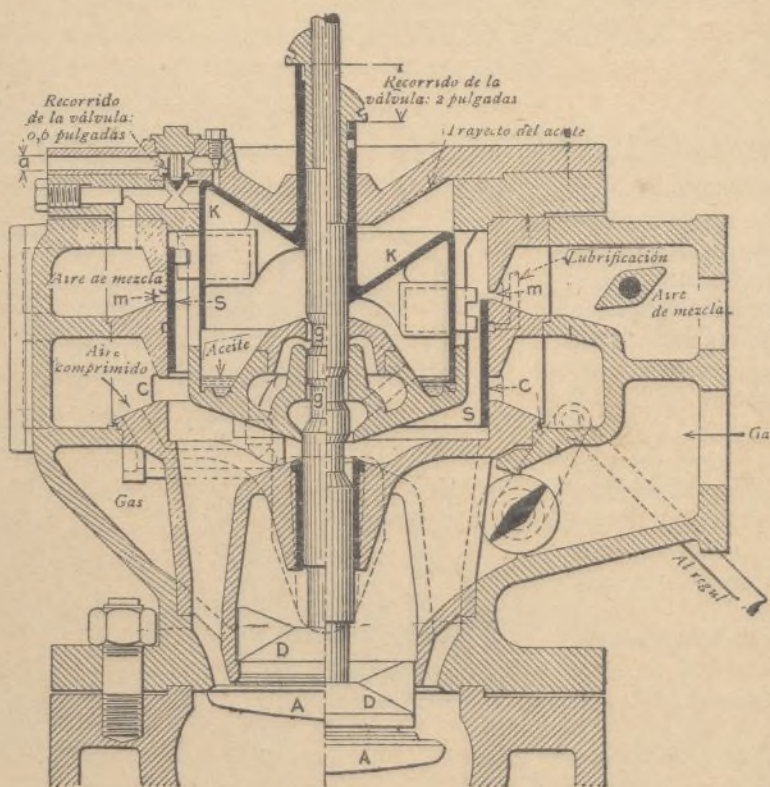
Válvulas combinadas de admisión é insuflación.
